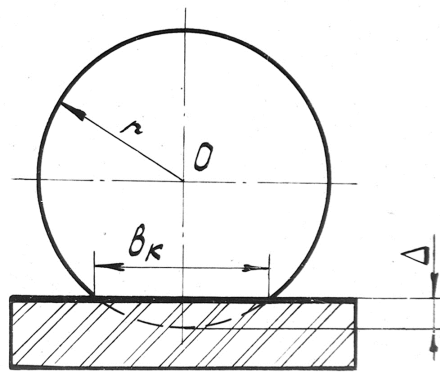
Схема контакту пелюсткового шліфувального круга з поверхнею заготовки
